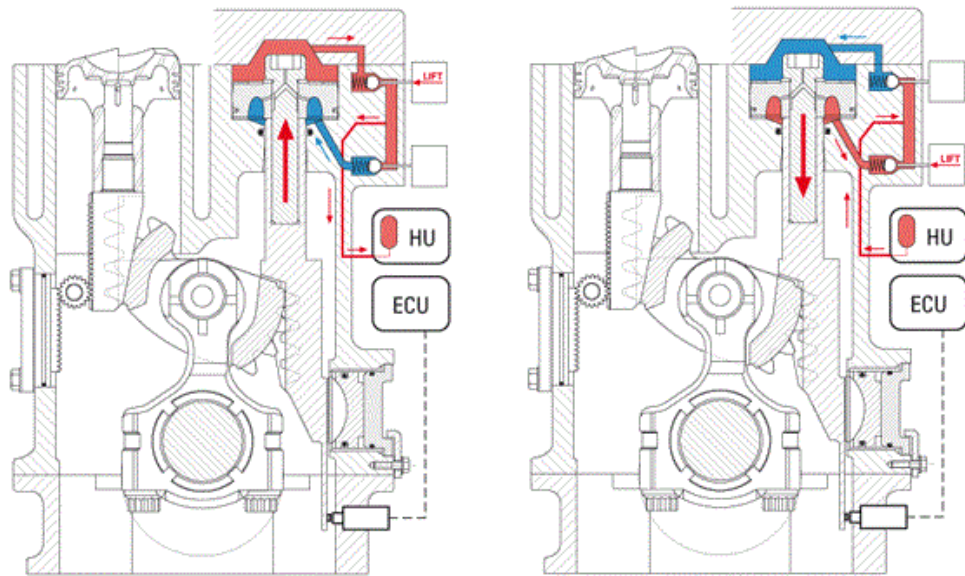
Vista em corte do mecanismo VCRI com destaque para o detalhamento do atuador hidráulico [8].
